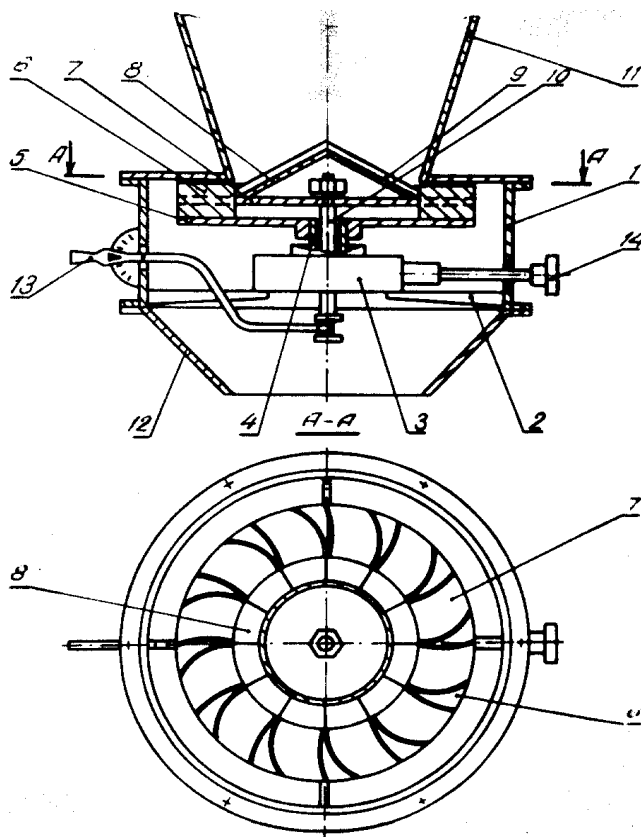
Конструктивна схема ротаційного дозатора: 1 – корпус; 2 – кронштейни; 3 – редуктор; 4 – трубчатий вал; 5 – дозуючий диск; 6 – направляючі елементи; 7 – рухоме дно; 8 – подаючий конус; 9 – лопаті; 10- рухомий вал; 11 – наддозаторний бункер; 12 – збиральний конус; 13 – регулювальна рукоятка; 14 – приводний вал редуктора
